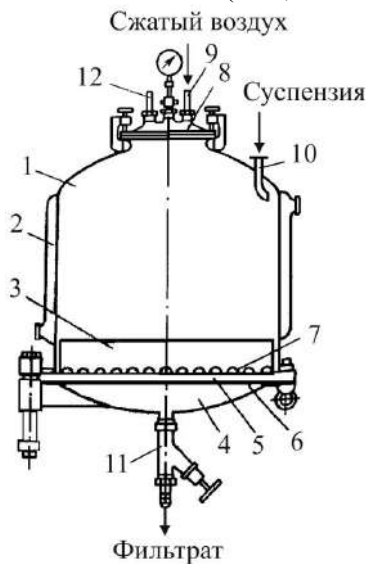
Нутч-фильтр, работающий под давлением: 1 – корпус; 2 – обогревающая рубашка; 3 – кольцевая перегородка; 4 – откидывающееся дно; 5 – фильтровальная перегородка; 6 – опорная решетка; 7 – сетка; 8 – съемная крышка; 9 – патрубок для подвода сжатого воздуха; 10 – труба для подачи суспензии; 11 – патрубок для отвода фильтрата; 12 – предохранительный клапан.
